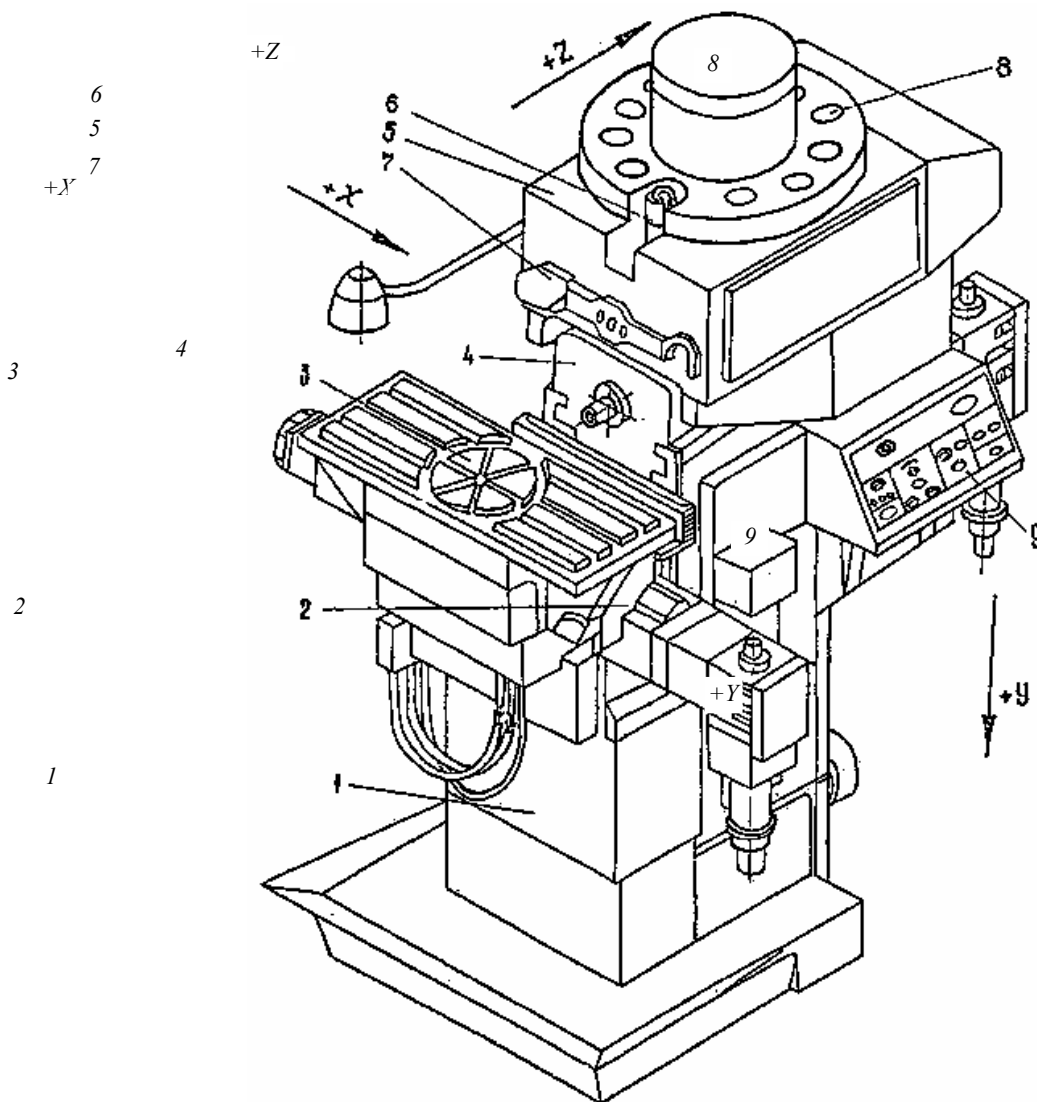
Многоцелевой станок MC12-2505. Направление координат станка
